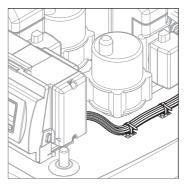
8. Fissare i cavi al serbatoio ad accumulo.
